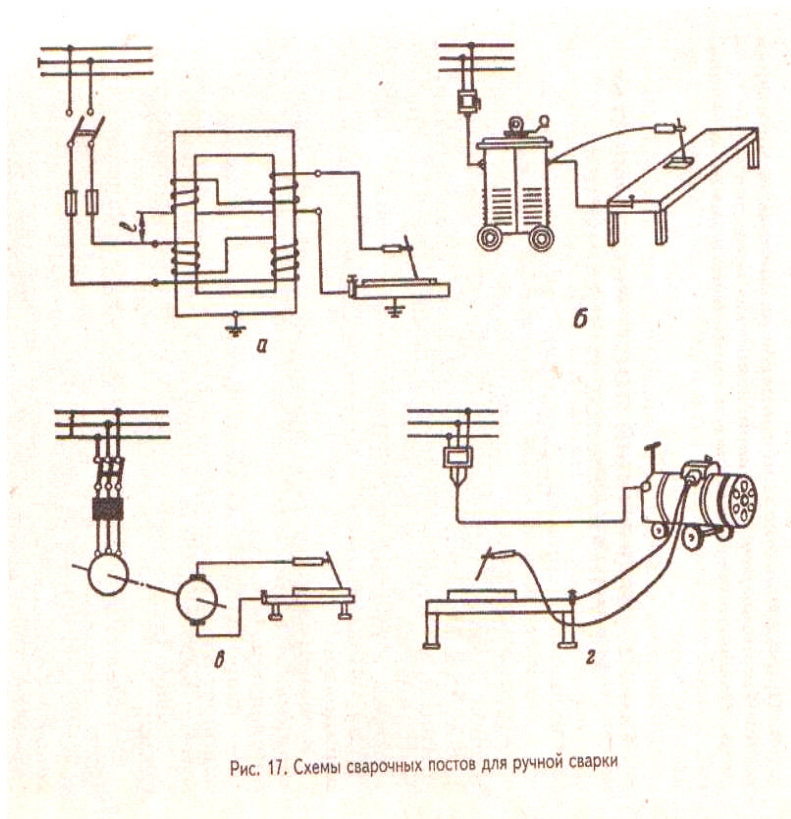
Схемы сварочных постов для ручной сварки
